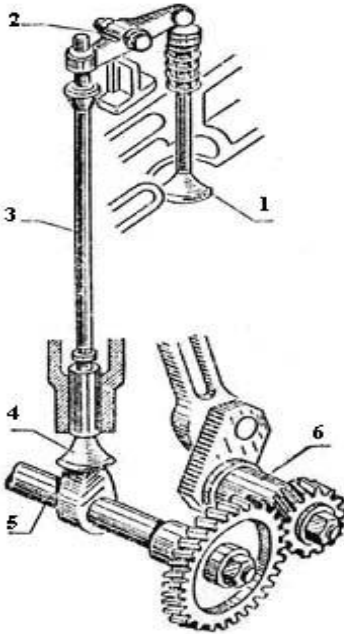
Механізм газорозподілу з верхніми клапанами:
